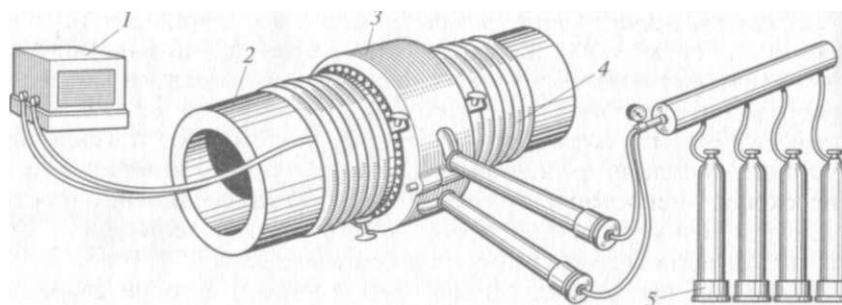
Термообработка сварных стыков кольцевой многофакельной горелкой:
